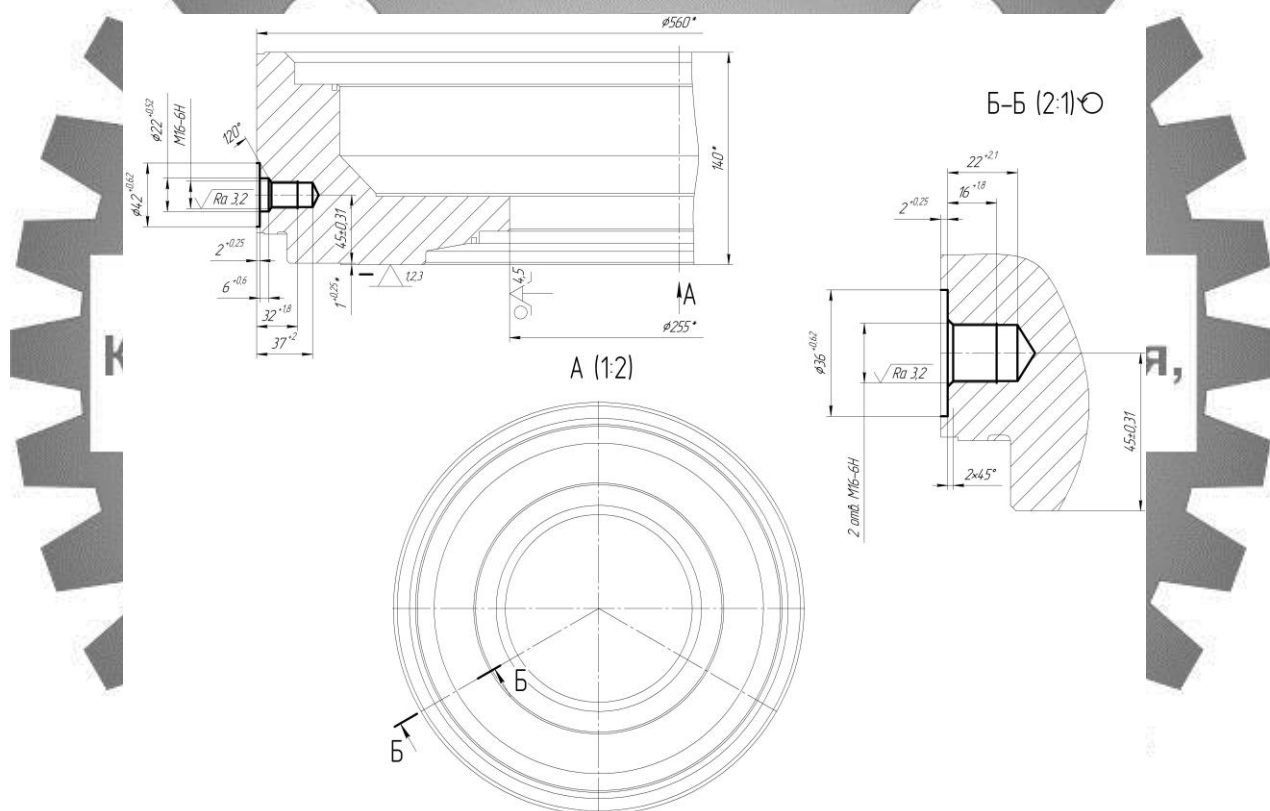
Схема базування заготовки на комплексній операції (перший варіант)
